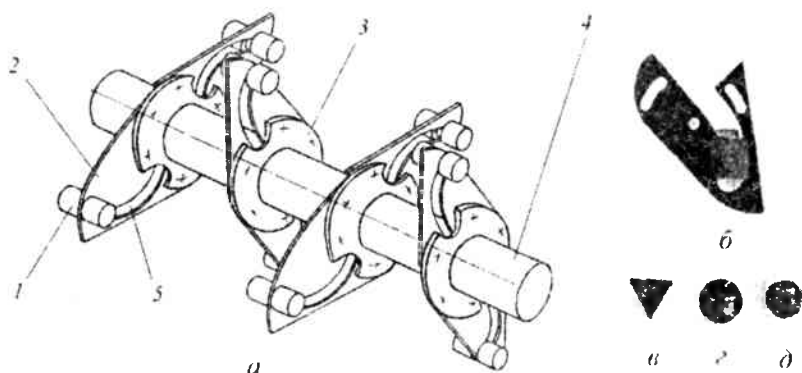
Комбинированный ротационный рабочий орган, снабженный кубическим (б), призма образным (в), цилиндрическим (г) и бочкообразным (д) деформатором: 1 – деформатор; 2 – плоский нож; 3 – диск; 4 – вал; 5 – паз
